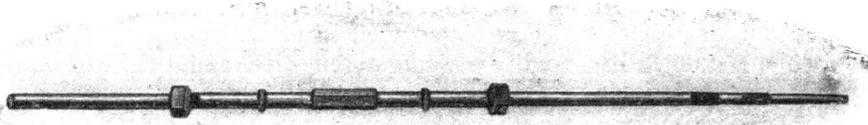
Kolbenschieberstange, älterer Ausführung.
